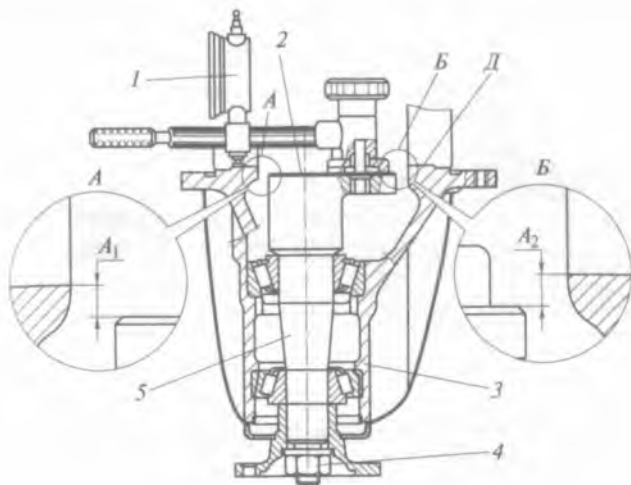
Схема определения толщины регулировочной прокладки (кольца) ведущего колеса:
